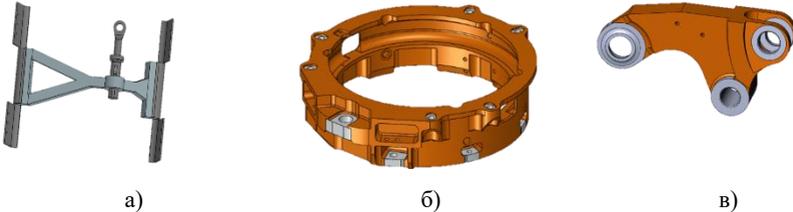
Типовые изделия, силовой конструкции ракеты
